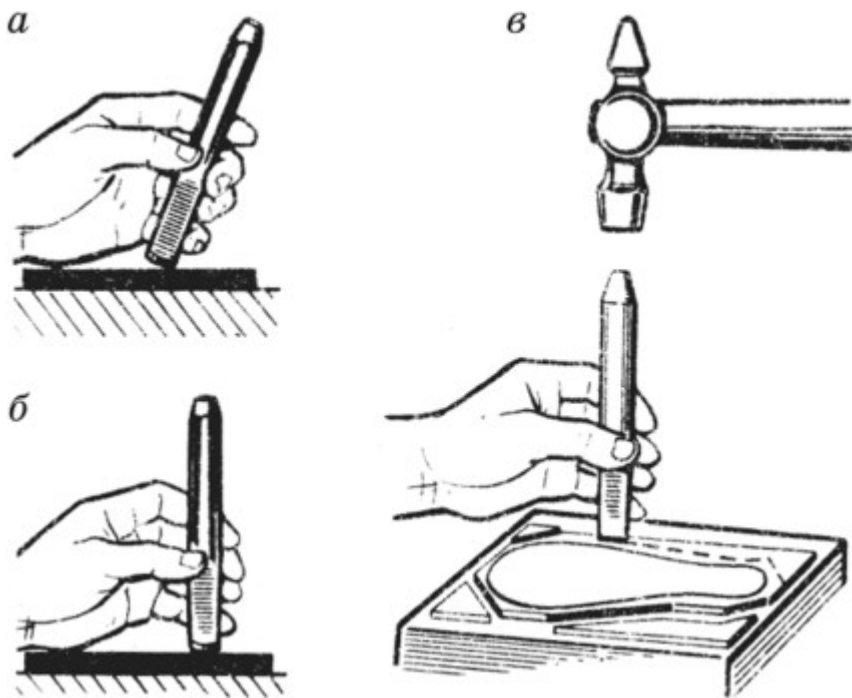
Установка зубила при рубке листового металла: а — начало установки; б — конец установки; в — прорубание по контуру
